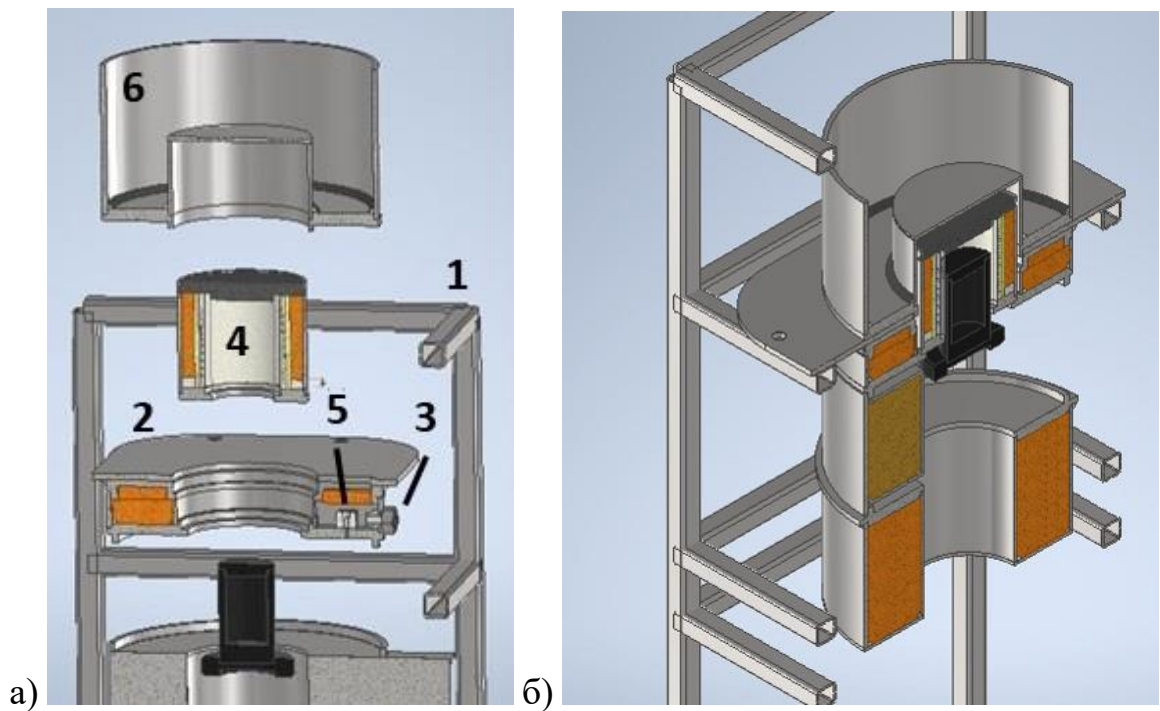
Конструкція з труб та токарних деталей: а – послідовність збірки частини печі; б – загальний вид проекту;
